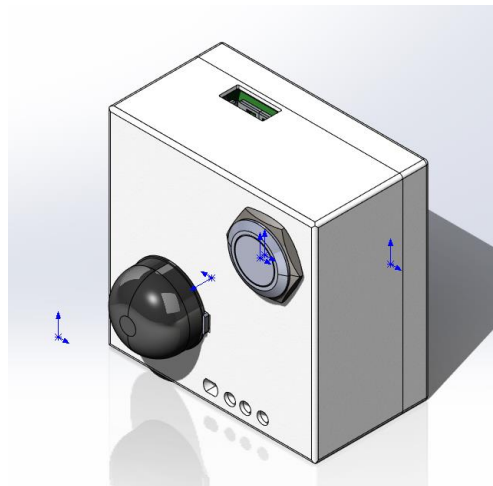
Ізометричний вид зібраного корпусу з платою
